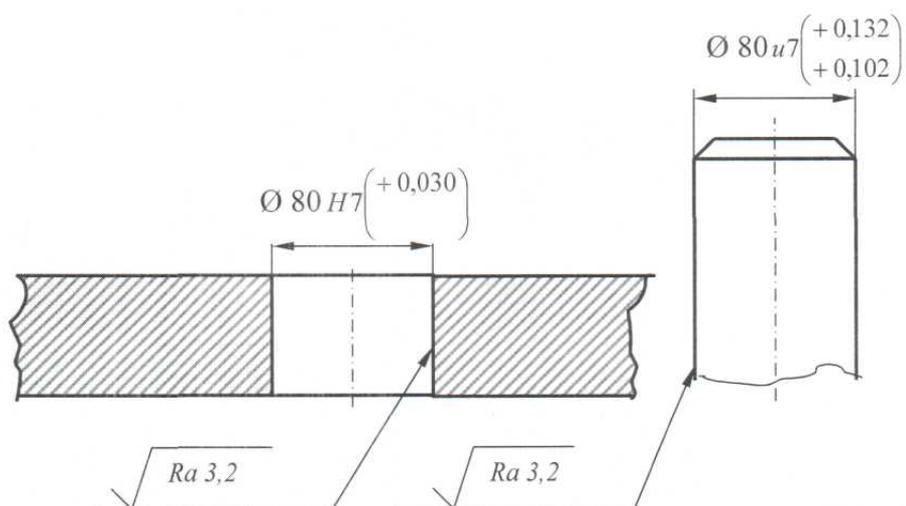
Обозначение допусков размеров на деталировочных чертежах
